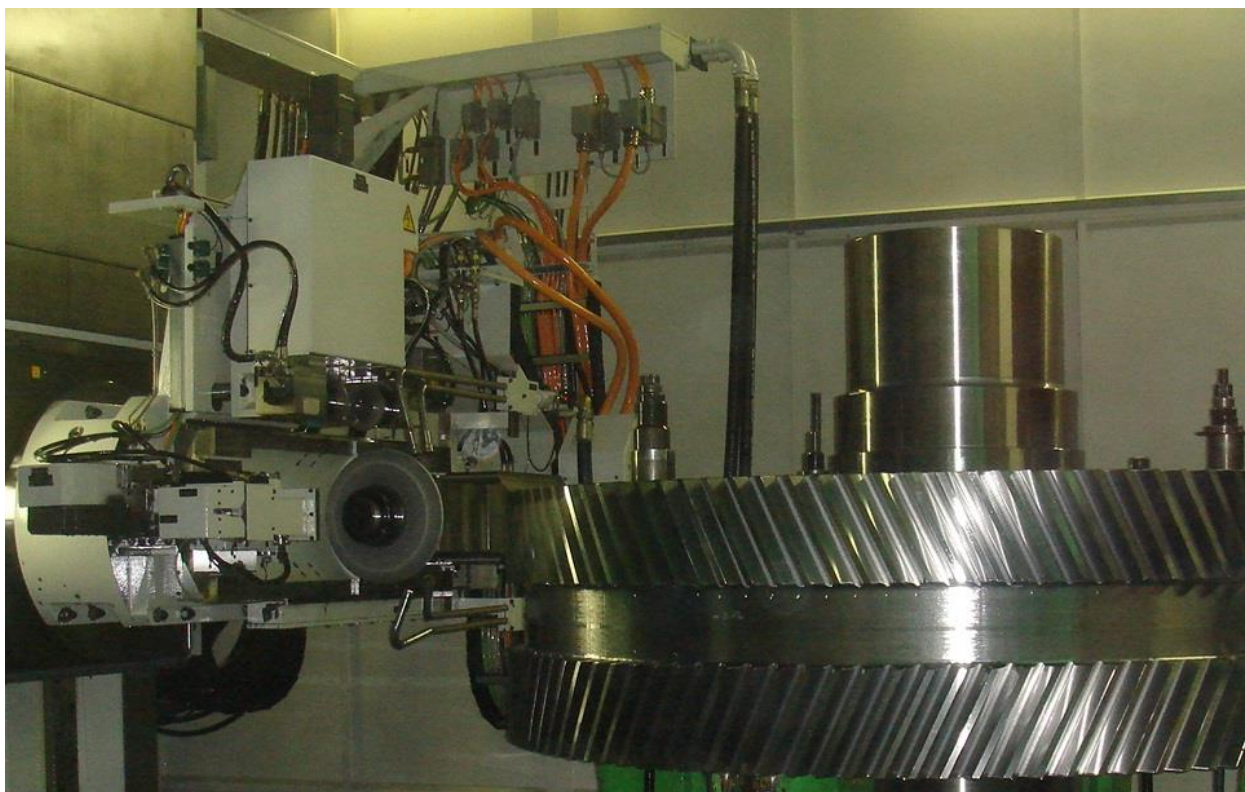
Зубофрезерування шевронних коліс на верстаті з ЧПУ
